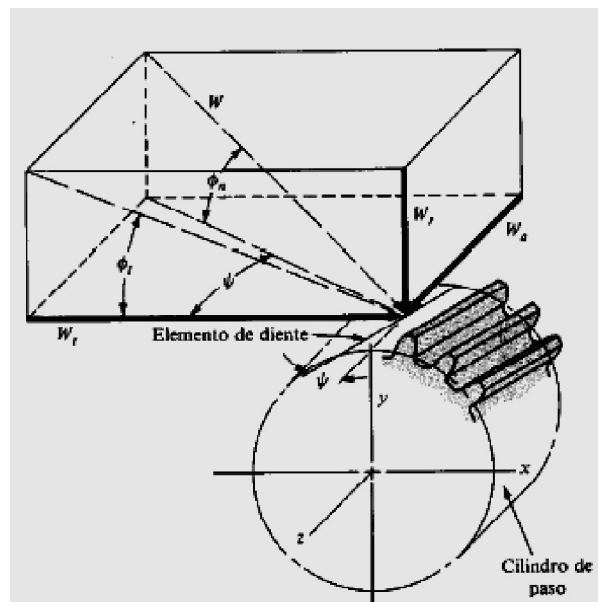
Fuerzas que actúan en el diente de un Engrane Helicoidal
